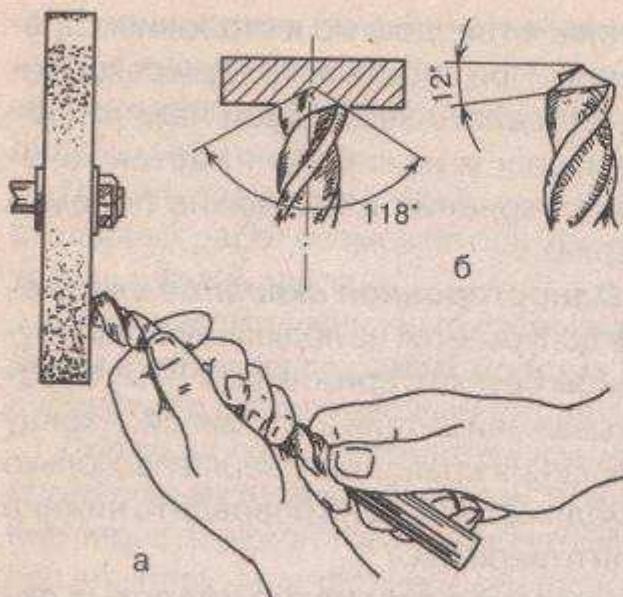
Заточка сверл: а — заточка сверла на точиле; б — проверка правильно-сти заточки по шаблону
